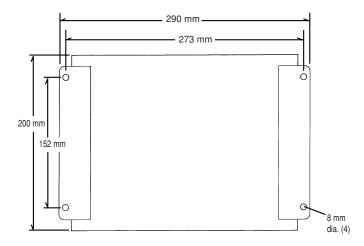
Dimensión de montura – Consola de válvula a motor
